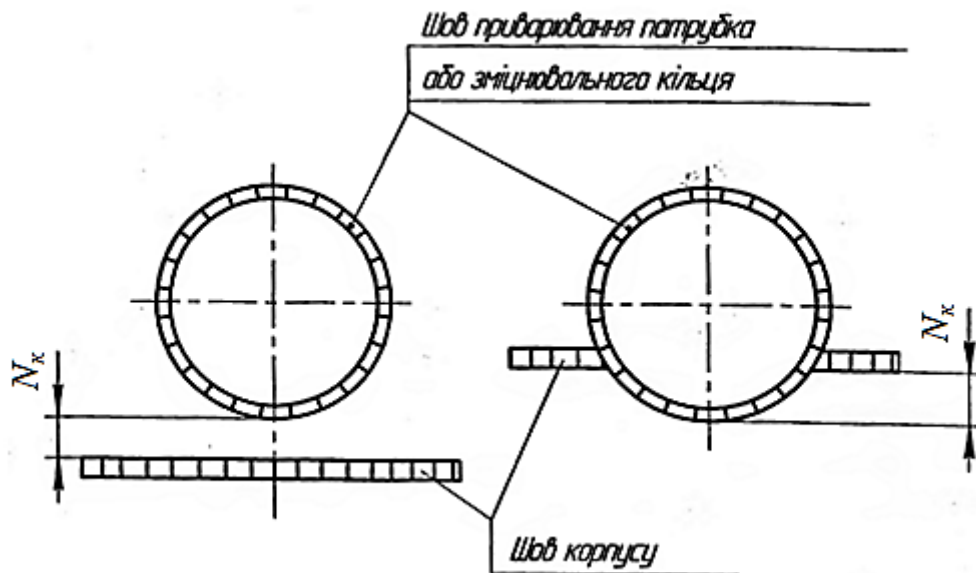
Схема визначення відстані між краєм шва корпусу та краєм шва приварювання деталі
